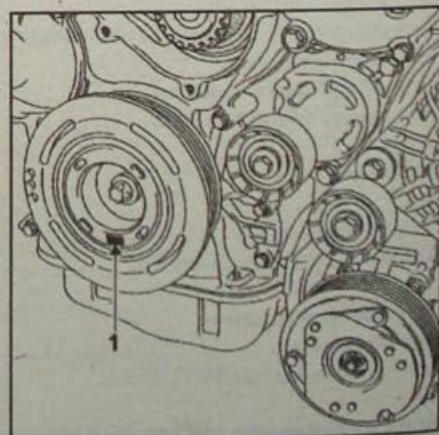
Расположение метки ВМТ (1) на шкиве коленчатого вала
